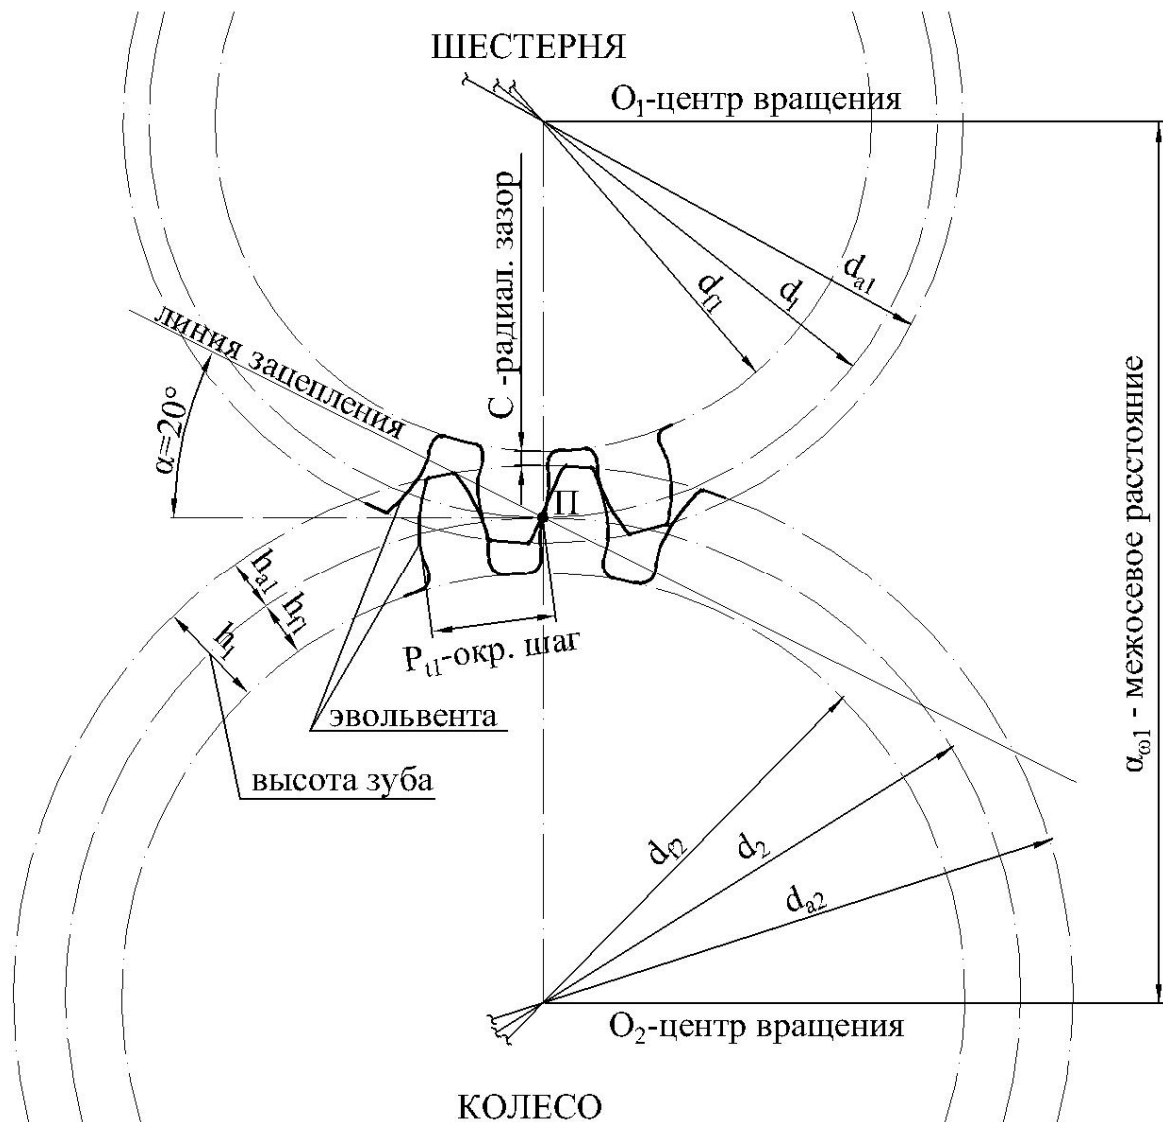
Основные геометрические параметры быстроходной зубчатой передачи
